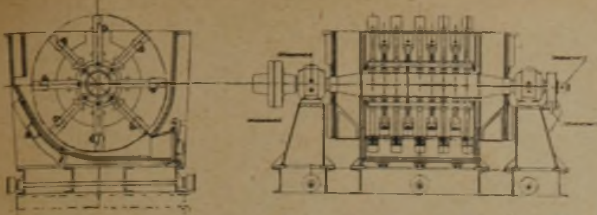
Babcock-Schlägermühle für Mühlenfeuerung
